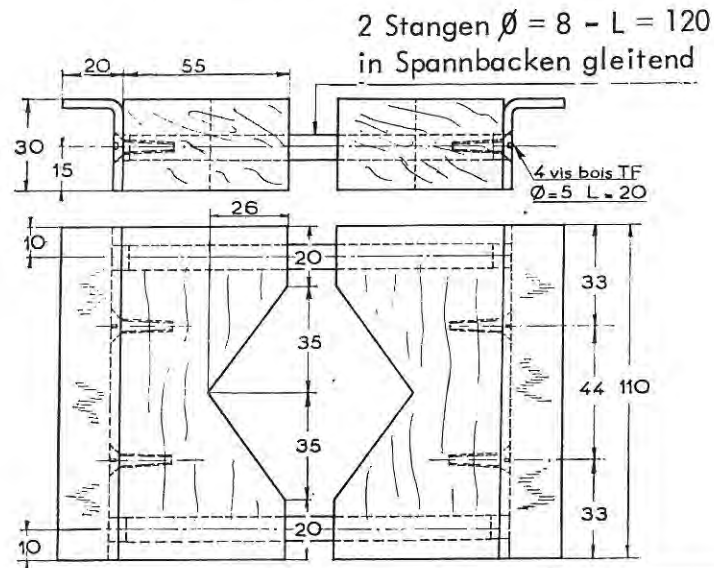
Halter für Federzylinder im Schraubstock - MR-3407-30
